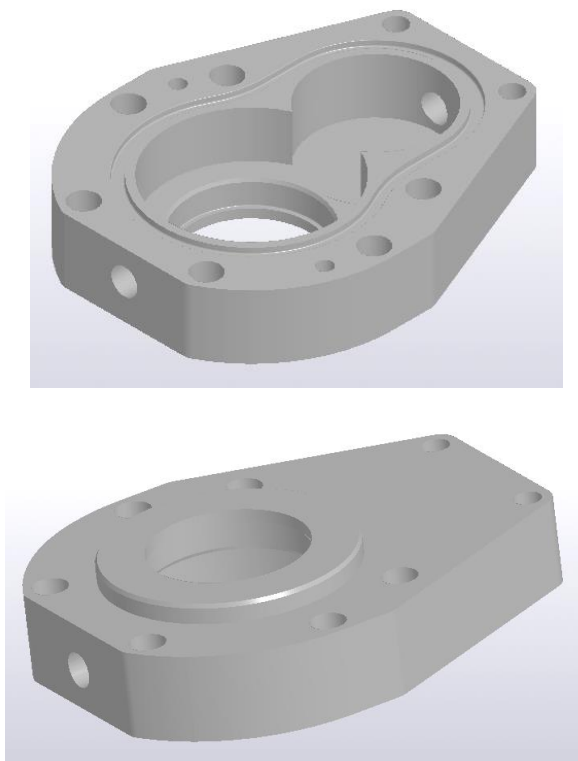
Деталь «Корпус RC11.1976.00.00»
